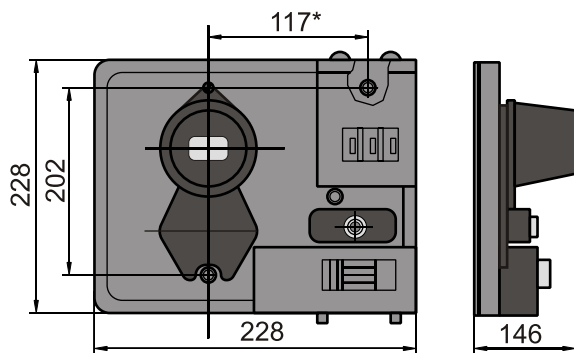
Внешний вид и габаритные размеры ЩК1109-01
